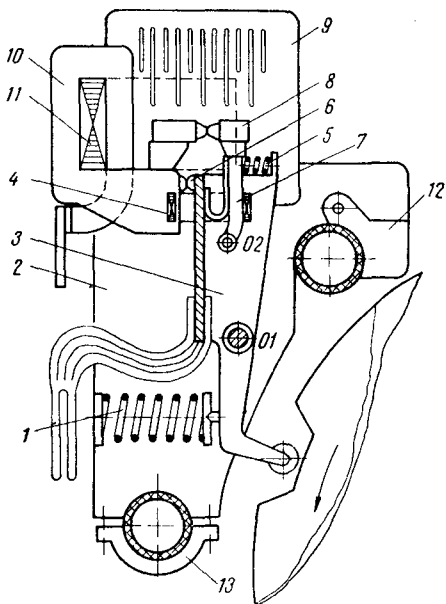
Устройство контакторного элемента с дугогашением контроллера ЭКГ-8
